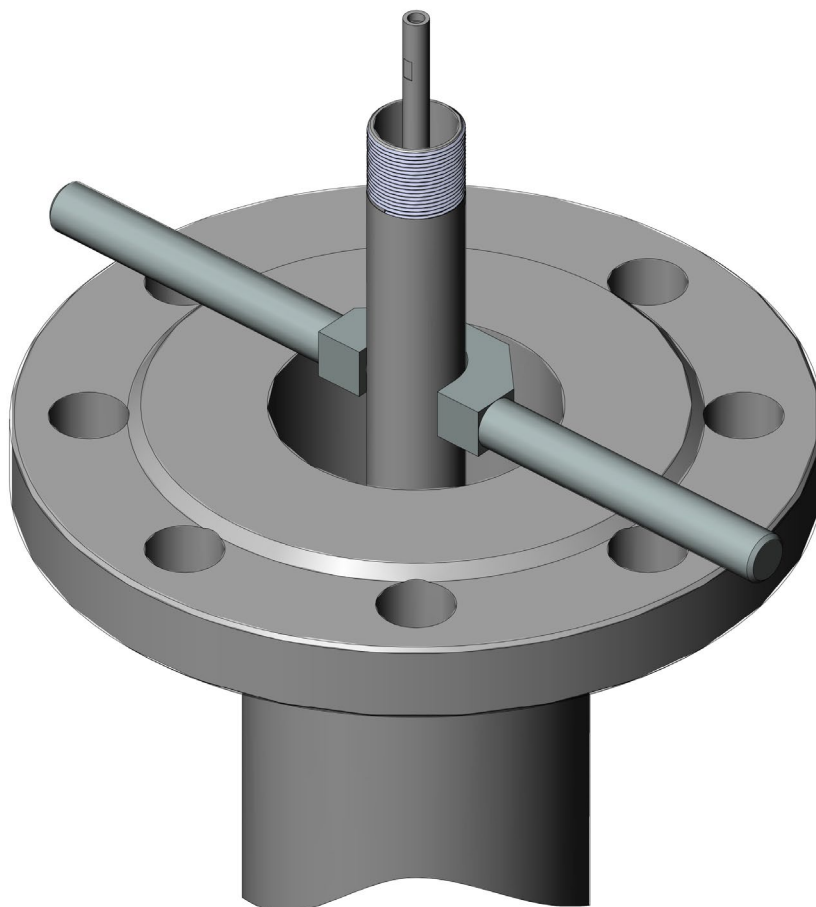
Погружение нижней секции в резервуар с опорой на приспособление
